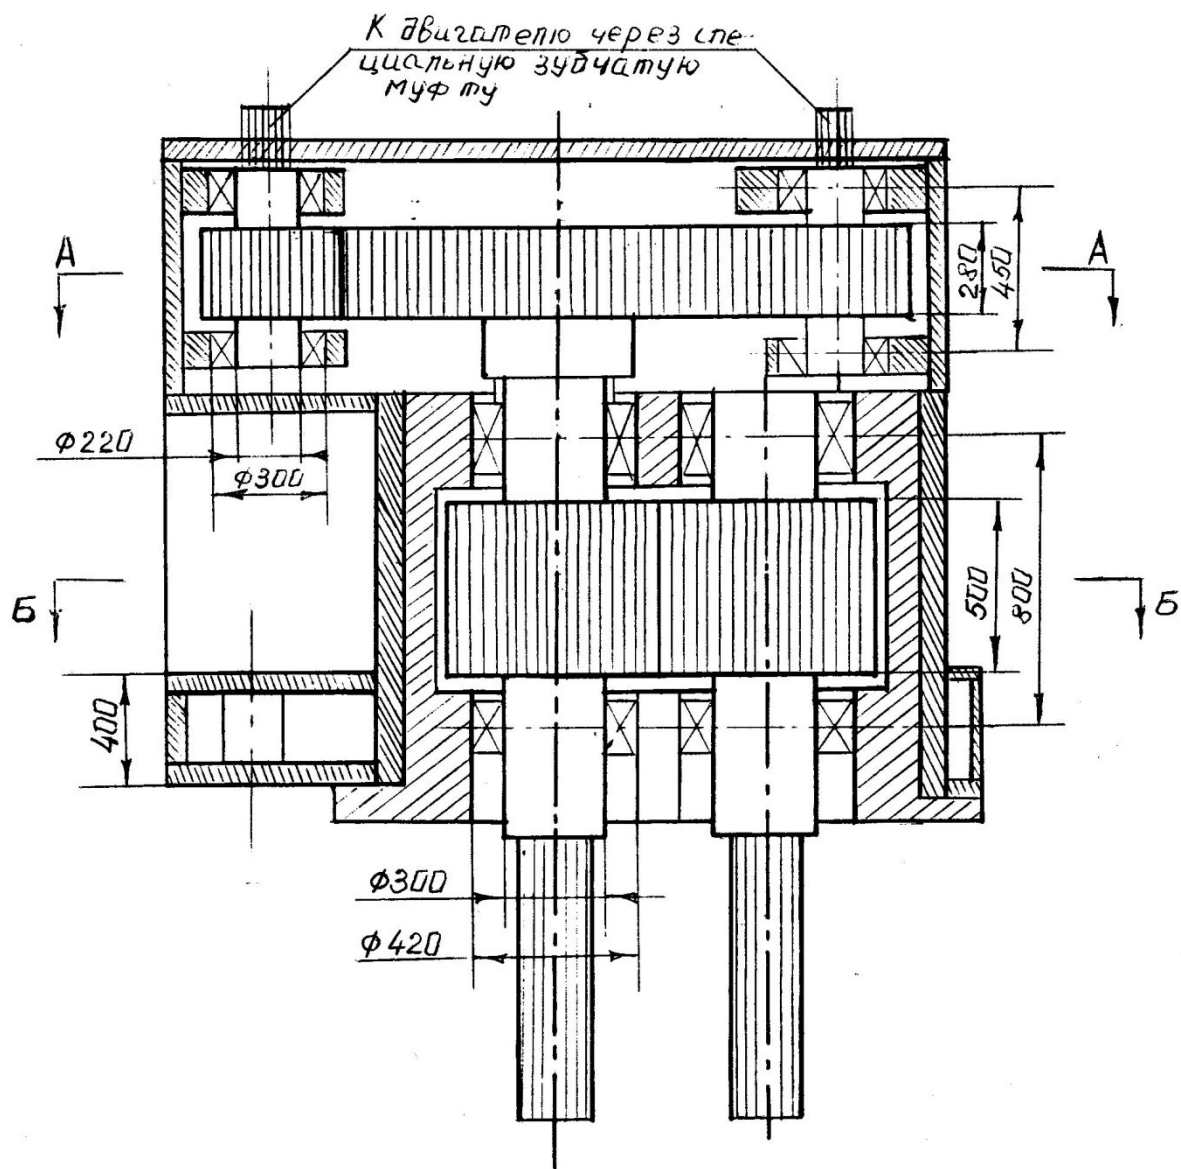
Многодвигательный привод вертикальной клетки прокатного стана
